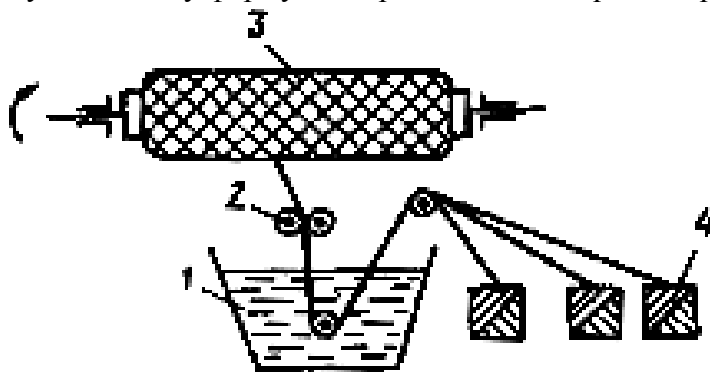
Схема намотування стрижня на машині токарного типу: 1 – ванна зі з'єднувачем; 2 – віджимні валики; 3 – заготовка; 4 – бавовняна тканина, нитки
